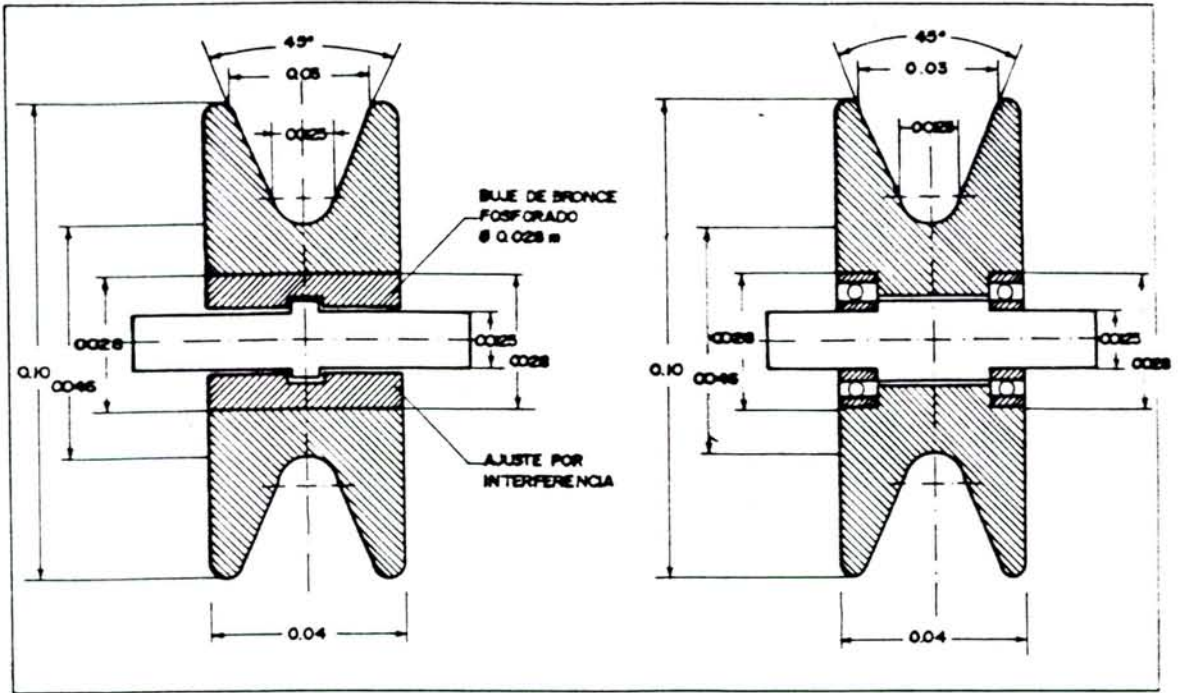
DETALLE CONSTRUCTIVO DE LAS POLEAS.
